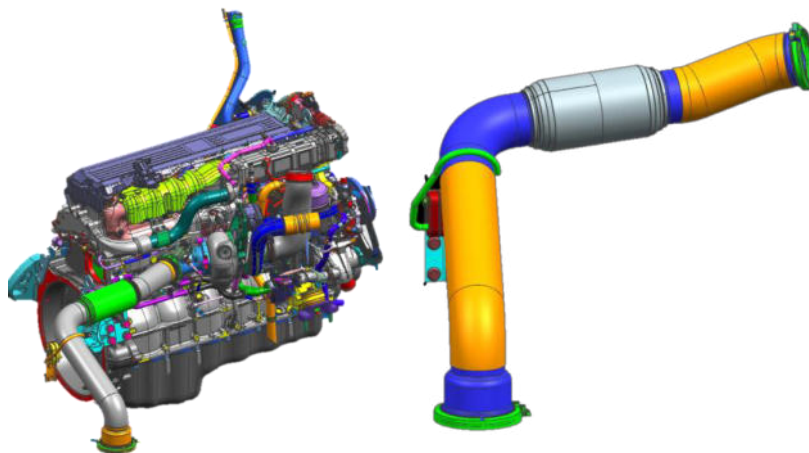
Modelo de ensamble CAD de un Motor de tractocamión y tubería de escape.
